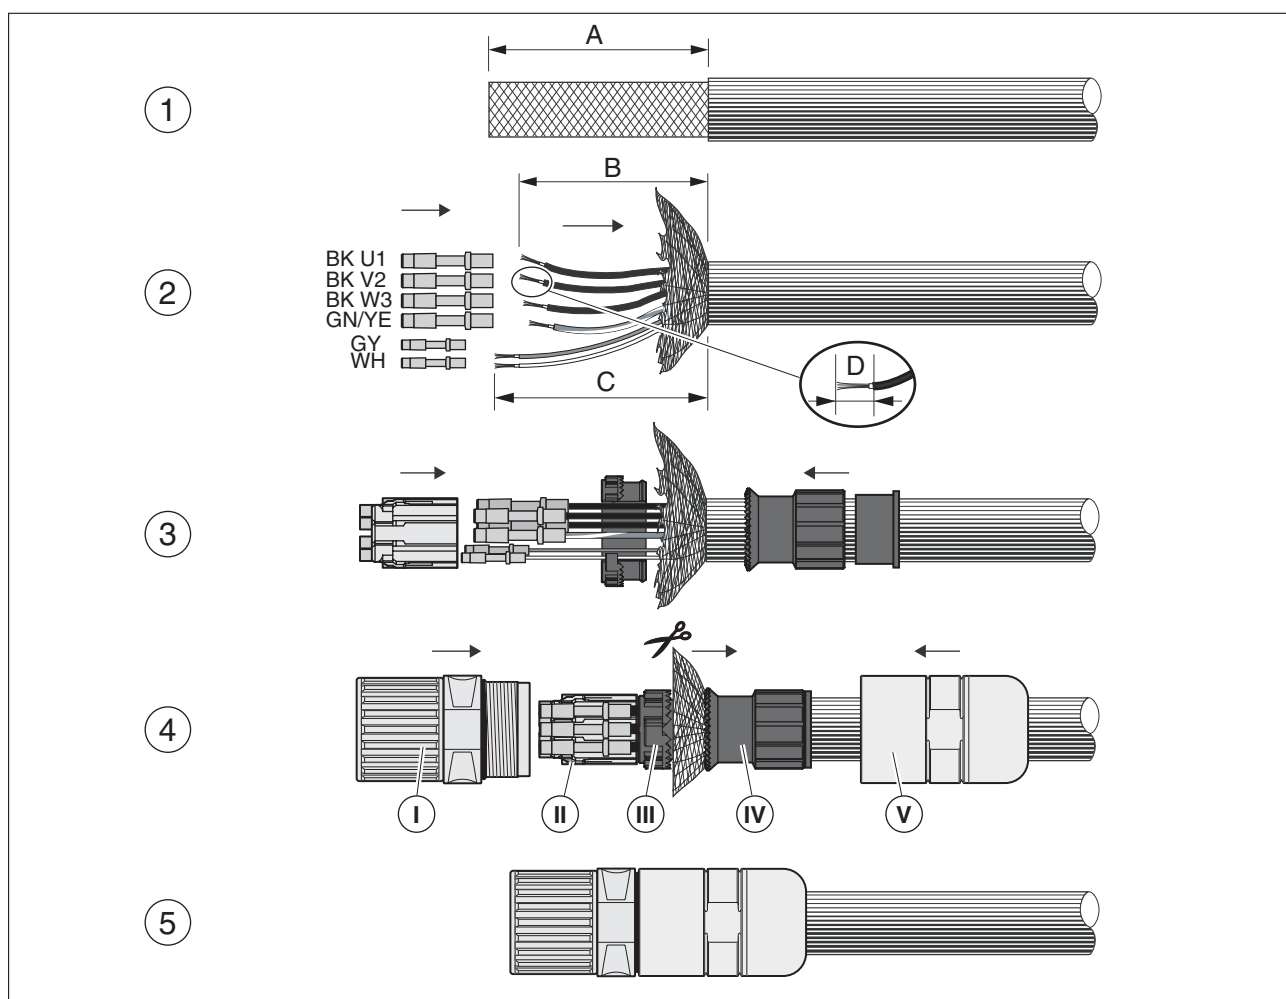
Assemblare il cavo motore con connettore motore M23
